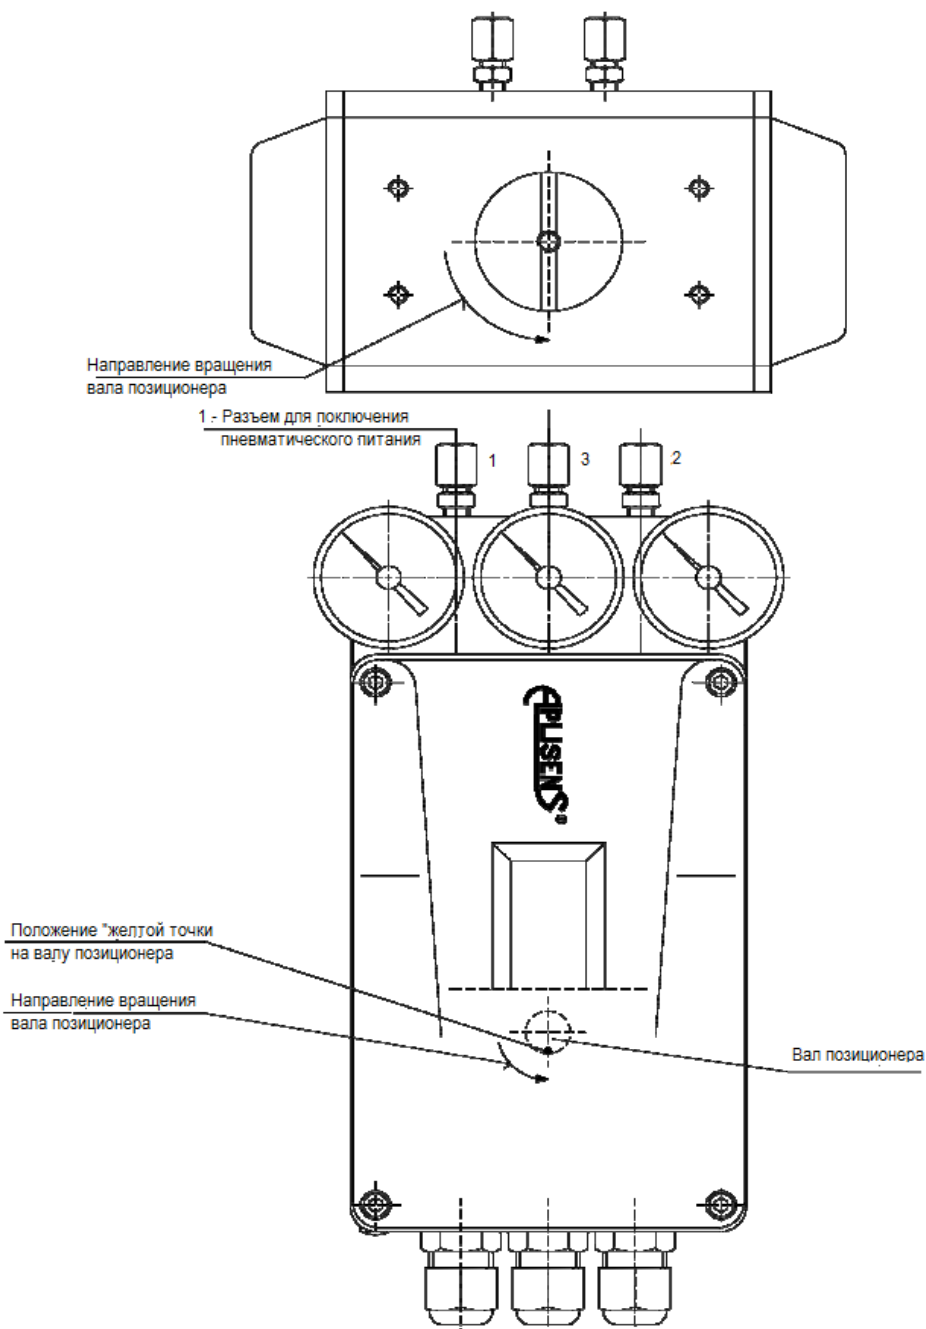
Монтажная позиция позиционера APIS-1X0-... и APIS-2X0-... относительно привода одинарного или двойного действия с вращательным движением.
